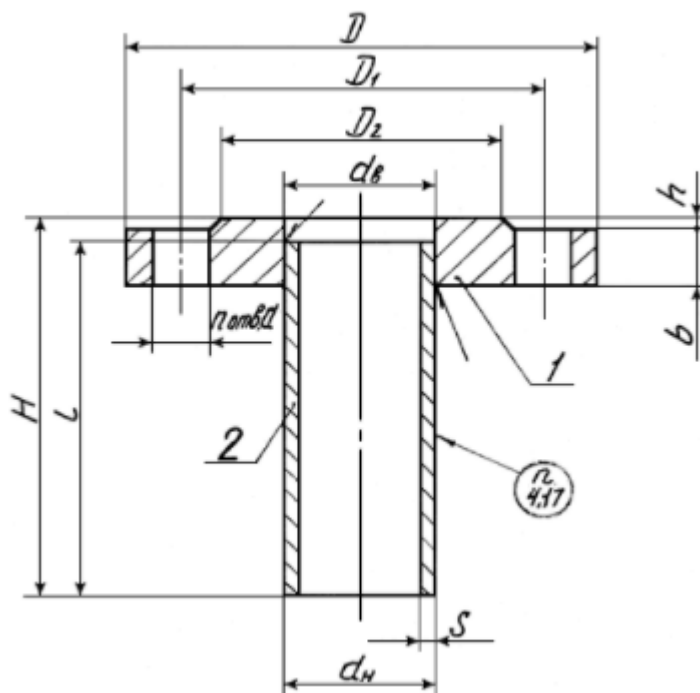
Штуцера с фланцами приваренными встык с соединительным ВЫСТУПОМ
